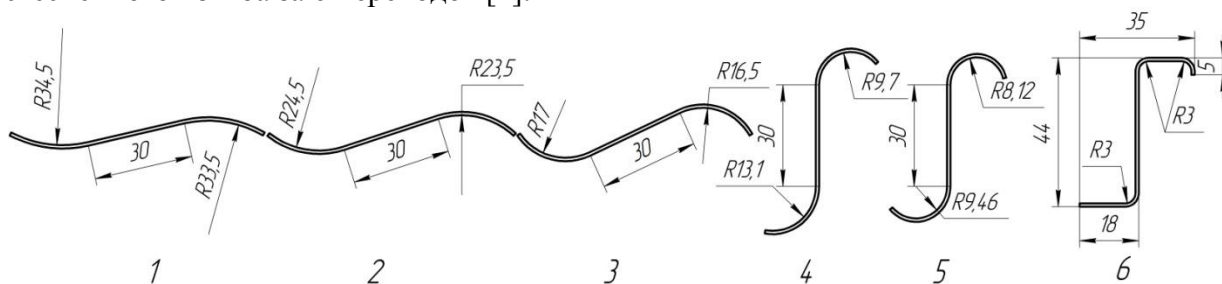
Схема переходов Z-образного профиля для заготовки шпангоута
